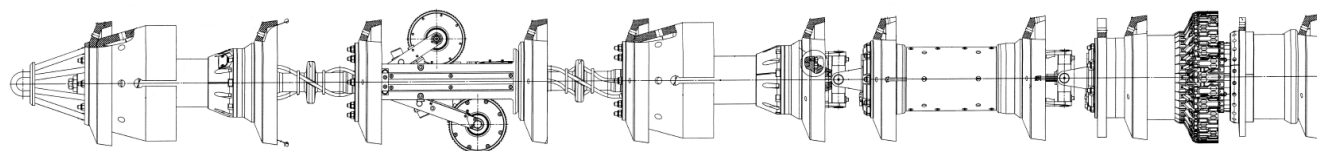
Чертеж общего вида дефектоскопа внутритрубного магнитного 8-MCK.01-00.000 и 8-MCK.01-00.000-01
